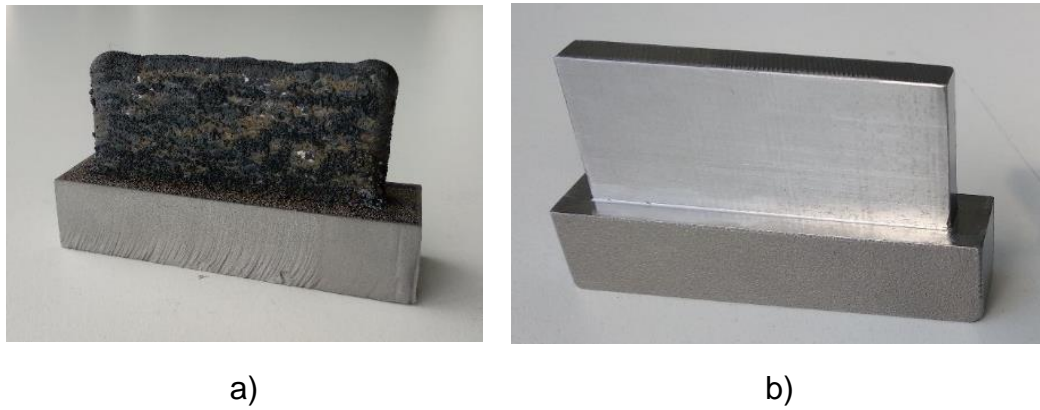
Paredes fabricadas: a) Aporte por láser; b) Mecanizando material forjado.
